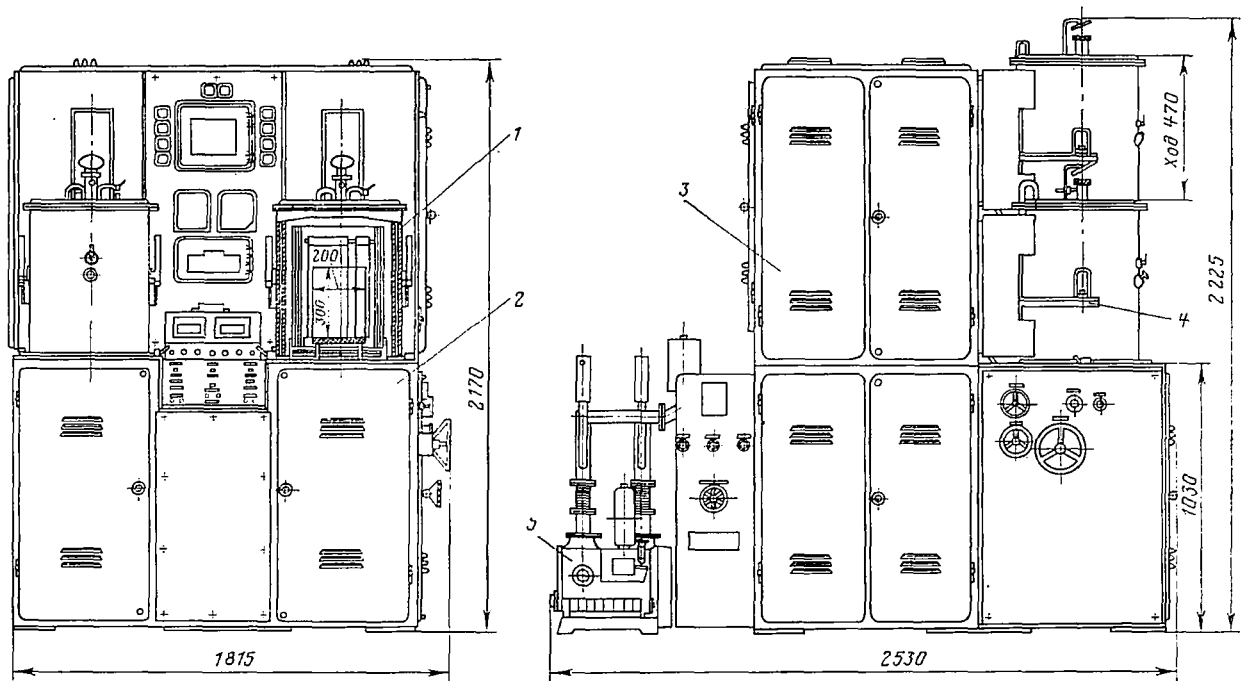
Общий вид печи СГВ-2,3/15Э-М1 (габаритный чертёж).
